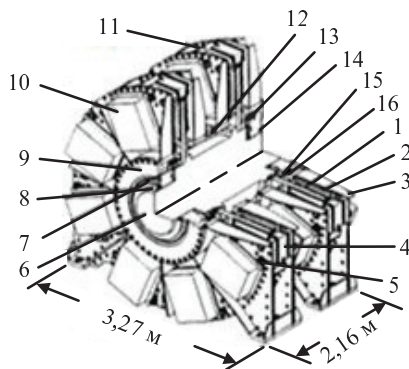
Высокогабаритный двухсторонний дисковый электродвигатель: 1 – ВПМ; 2 – статорный узел; 3 – корпус; 4 – ударный демпфер; 5 – амортизатор; 6 – вал ротора; 7 – зажим диска ротора; 8 – уплотнительный узел вала; 9 – держатель подшипника; 10 – сегмент статора; 11 – центральный каркас; 12 – распорка; 13 – диск ротора; 14 – подшипниковый узел; 15 – уплотнитель ротора; 16 – уплотнительный узел ротора
